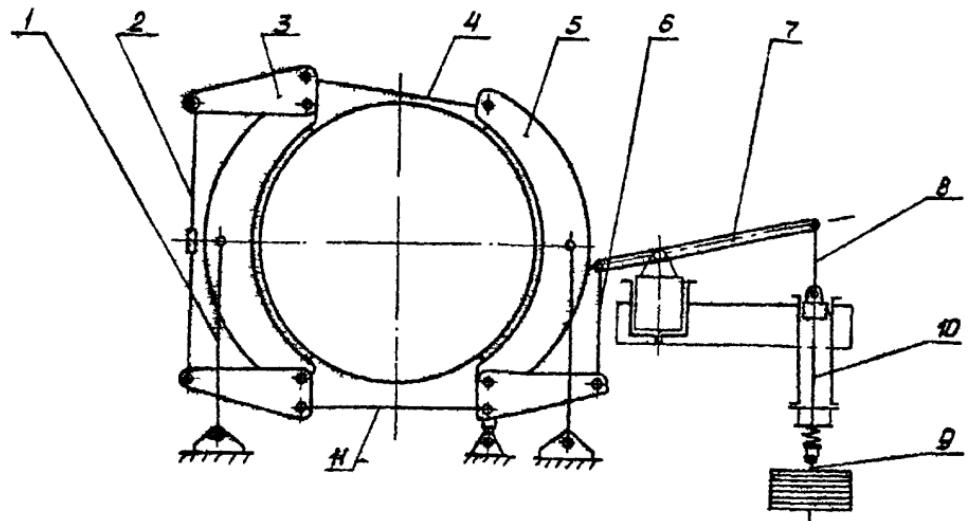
Тормоз с комбинированным приводом (рабочий - пневматический, предохранительный - гидромоторовой) крупных подъемных машин НКМЗ ЦР-4х3/0,7; 2Ц-4х1,8; 2Ц-4х2,3; ЦР-5х3/0,6; 2Ц-5х2,4; 2Ц-5х2,8; ЦР-6х3/0,6; 2Ц-6х3,4/0,6; 2Ц-6х2,4; 2Ц-6х2,8; БЦК-8/5х2,7; БЦК-9/5х2,5: I - стойка; 2,6 - вертикальная тяга; 3 - угловой рычаг; 4,11 - горизонтальная тяга; 5 - тормозная балка; 7 - дифференциальный рычаг; 8 - штанга; 9 - тяга грузов; 10 - шток.
